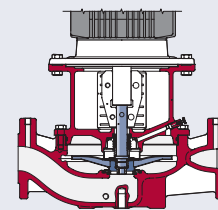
Вертикальный одноступенчатый моноблочный насос «ин-лайн»
